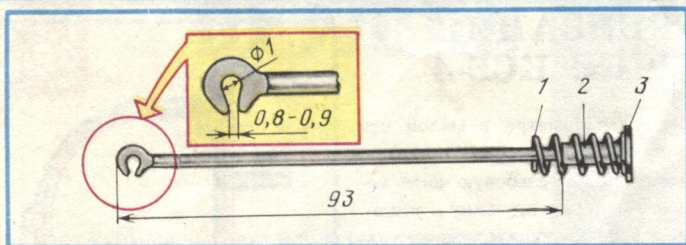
Толкатель: 1 — пружина для возврата толкателя; 2 — ниппель спицы; 3 — припаянная шайба.
